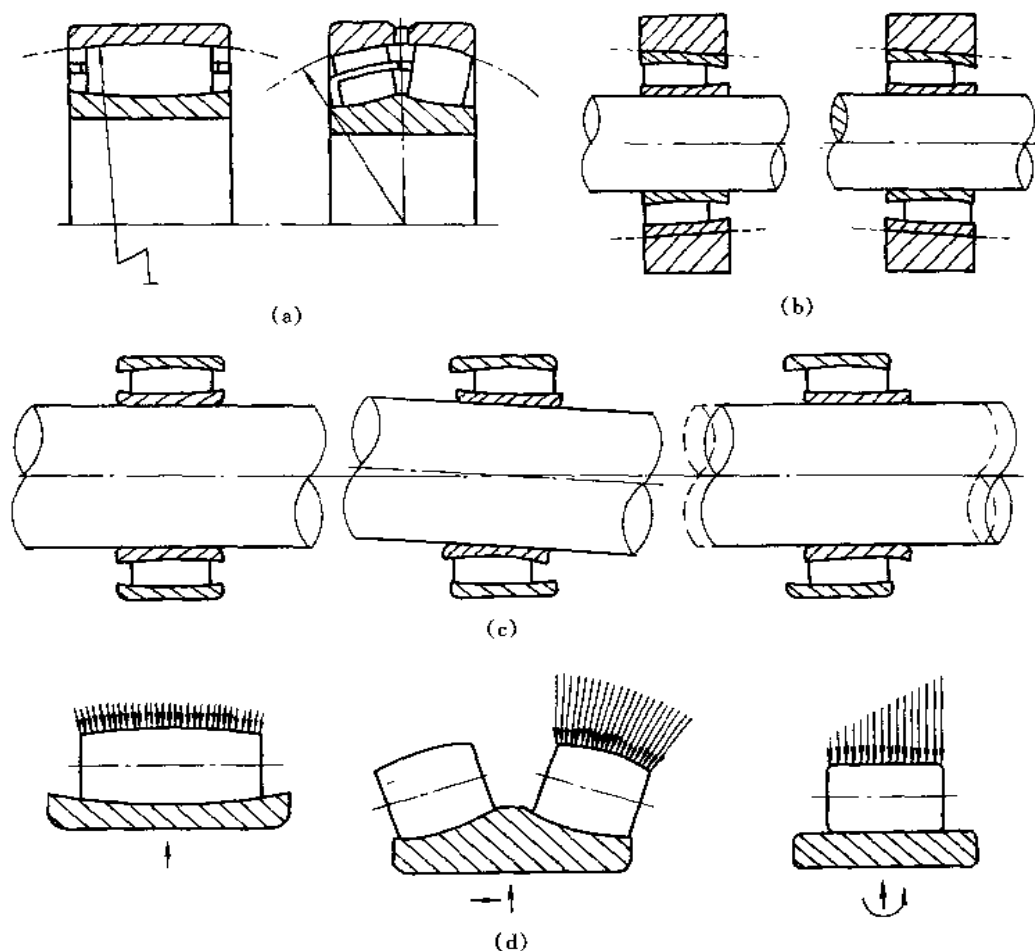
CARB 型轴承与传统轴承的比较 (SKF 公司新产品资料)
